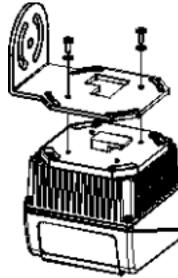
Befestigung der Baugruppe am Montagewinkel
